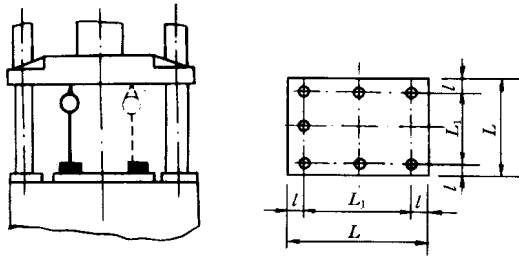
检验活动横梁（滑块）下平面与工作台上平面的平行度
